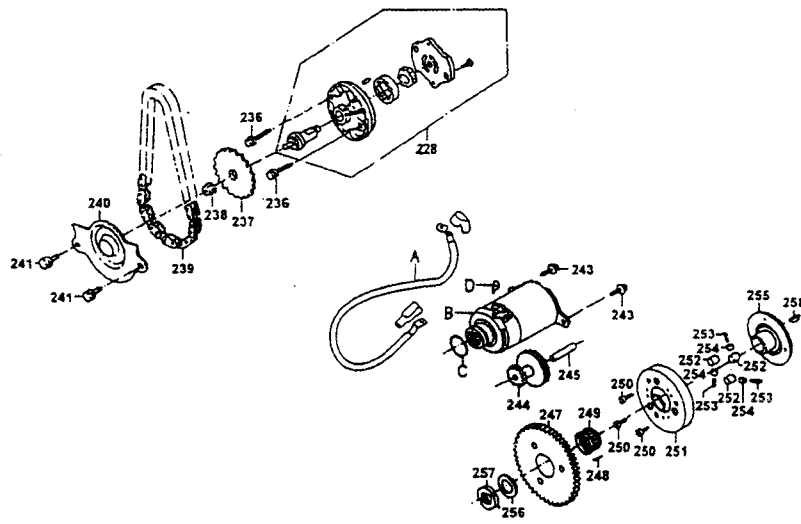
起动机.机油泵 STARTING MOTOR.OIL PUMP
